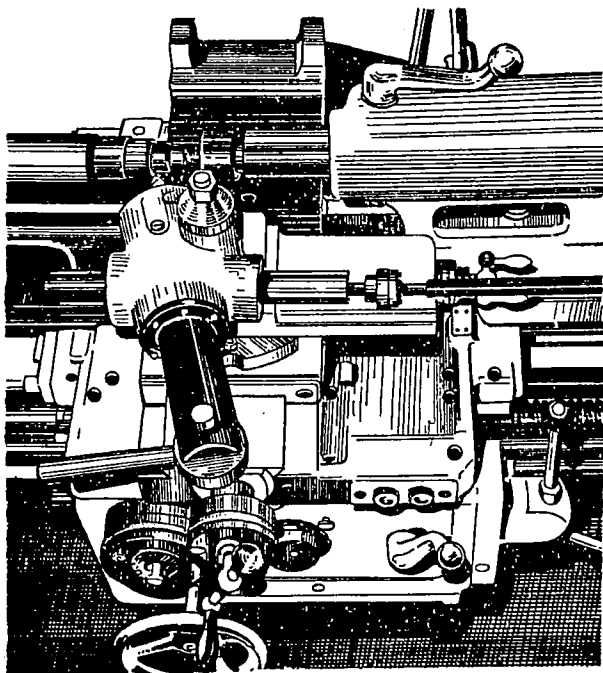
Полуавтоматическое копировальное приспособление для обточки ступенчатых валов, установленное на станке.
